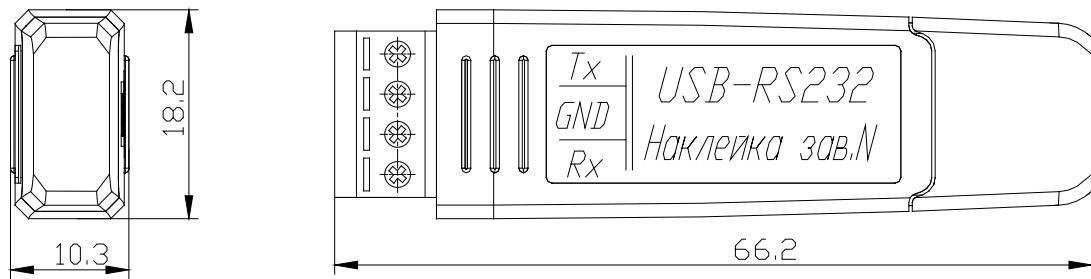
Внешний вид и габаритные размеры преобразователя «USB-RS485»
